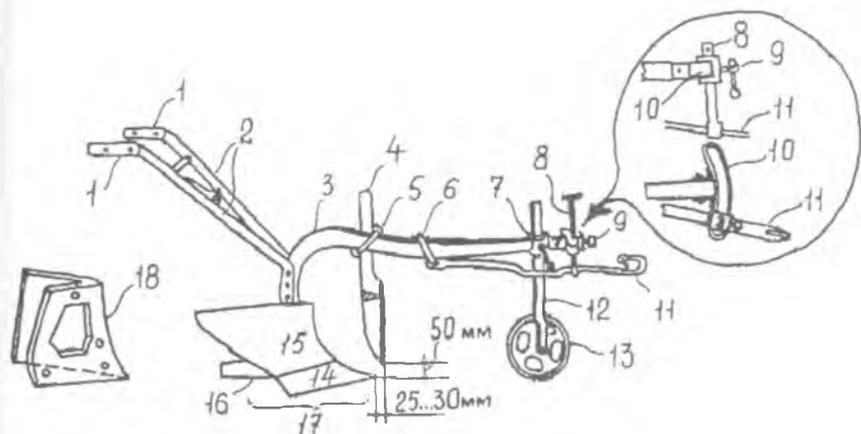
Конный висячий плуг: 1 - деревянные ручки рукояток; 2 - рукоятки; 3 - грядиль; 4 - черенковый нож; 5 - скоба крепления ножа; 6 - гнездо грядиля для крепления тягового крюка; 7 - хомут установочного колеса; 8 - рейка установочная; 9 - стопорный болт; 10 - дугообразная скоба; 11 - тяговый крюк; 12 - стойка установочного колеса; 13 - колесо; 15 - отвал; 16 - полевая доска; 17 - корпус плуга; 18 - стойка низкая
